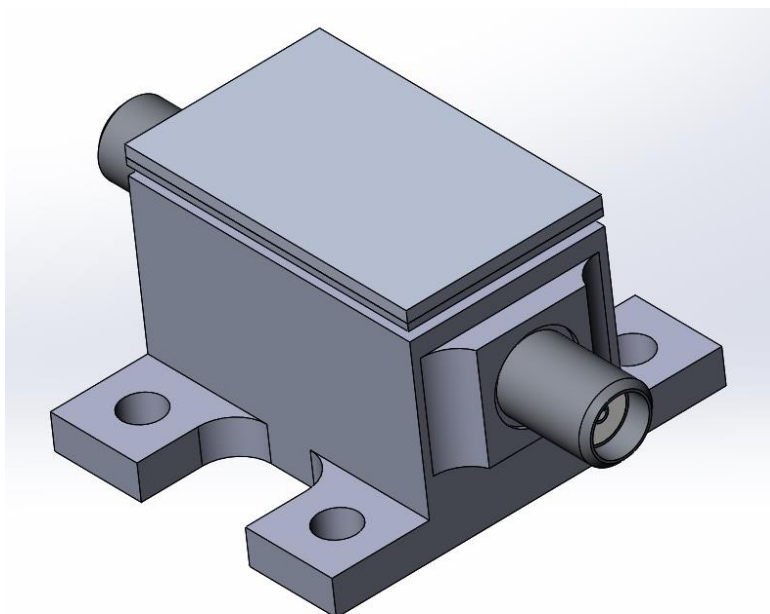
Корпус режекторного фильтра на основе короткозамкнутых кольцевых резонаторов, в сборе
